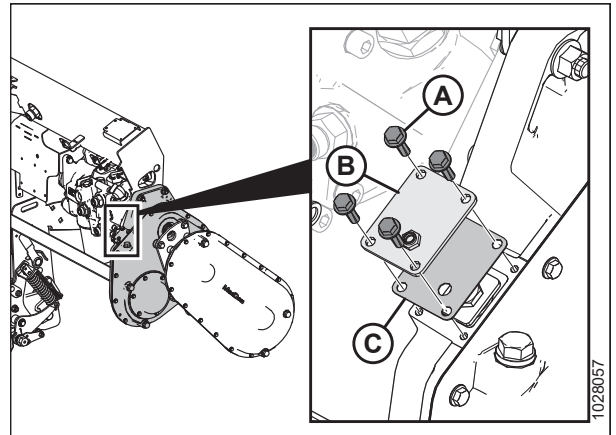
Кришка натягувача ланцюга головного редуктора
